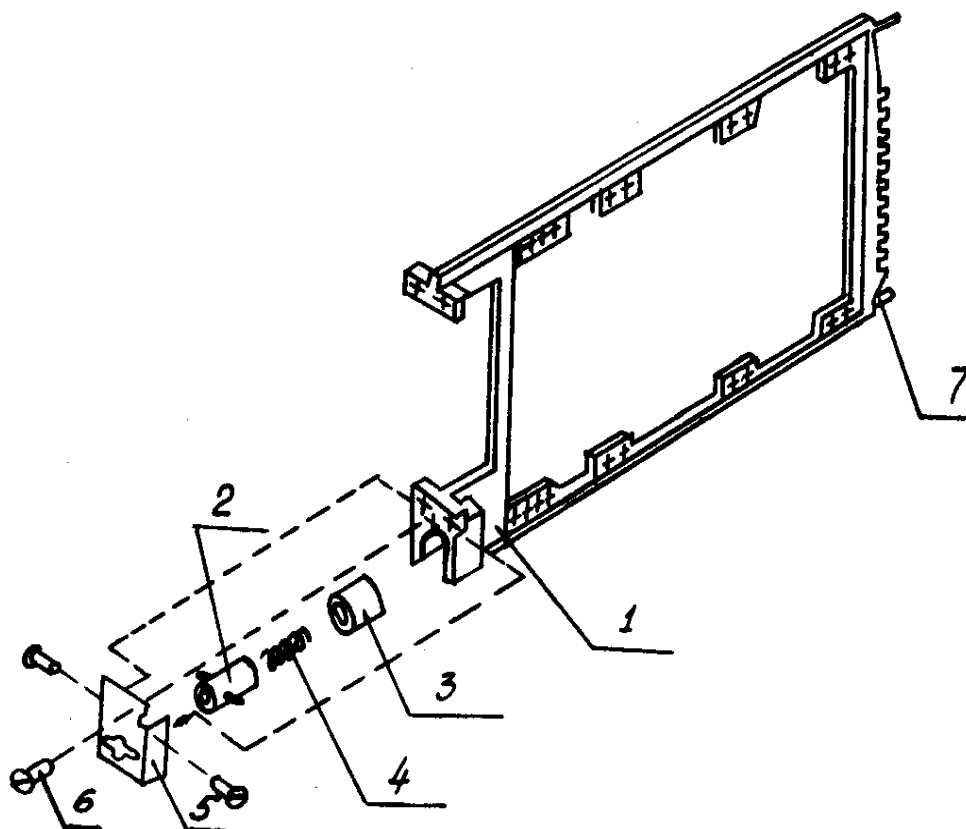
Рамка кассеты: 1 - рама; 2 - затвор; 3 - кулачок; 4 - пружина; 5 - планка; 6 - винт М3х6; 7 - ловитель
